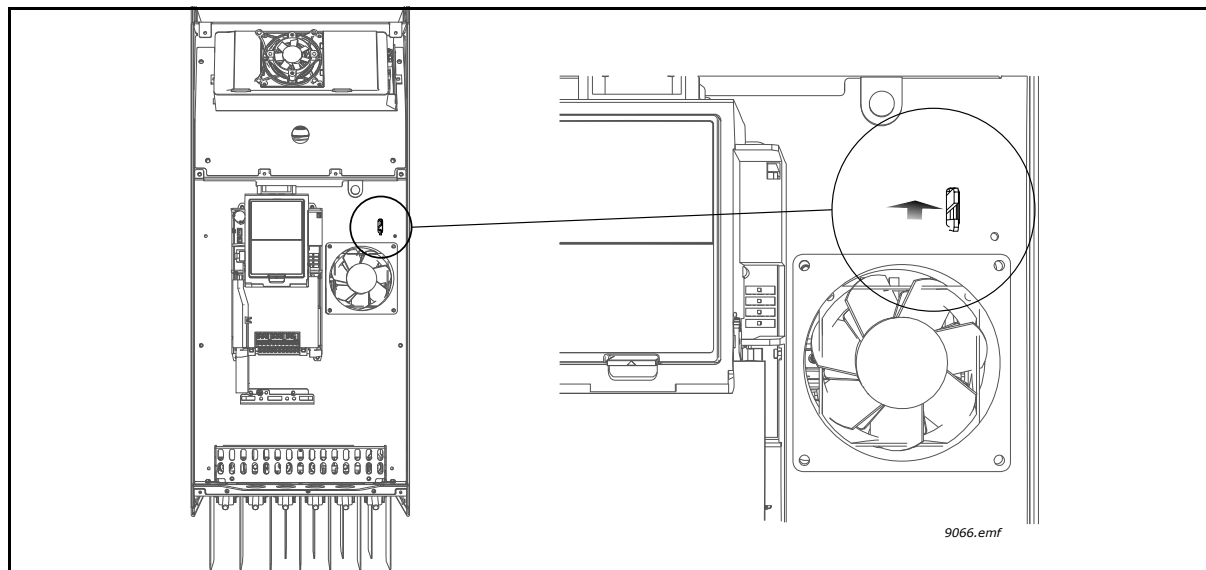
De jumper verwijderen; MR6 dient als voorbeeld
